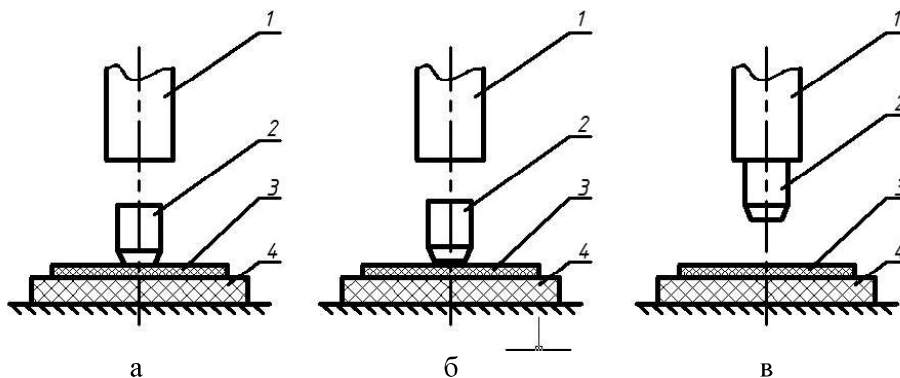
Схема передачі енергії від ударника пресу через робочий інструмент матеріалу: 1-ударник; 2-робочий інструмент; 3-матеріал; 4-основа (вирубна плита)
